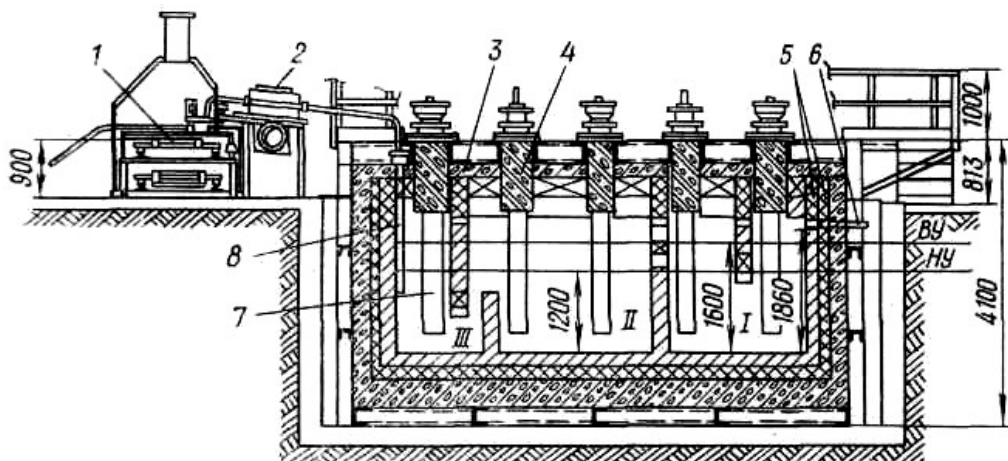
Литейный комплекс для непрерывного рафинирования и разливки магния: 1 – литейный конвейер; 2 – электромагнитный насос; 3 – печь; 4 – теплоизолирующие трубки; 5 – футеровка; 6 – загрузочный патрубок; 7 – нагревательные элементы; 8 – заборный патрубок для магния; ВУ и НУ – верхний и нижний уровни металла
